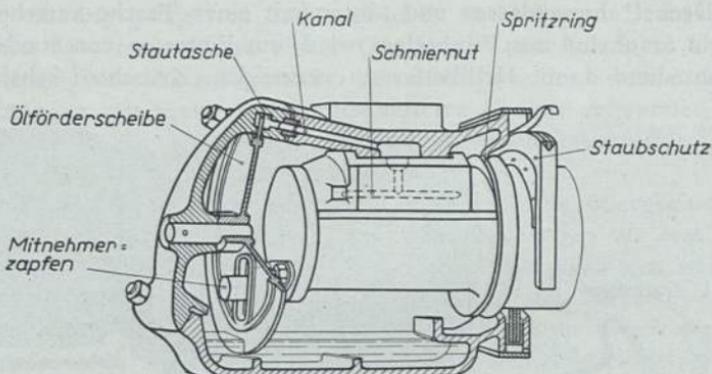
Tenderachslager mit Druckumlaufschmierung Bauart Friedmann
